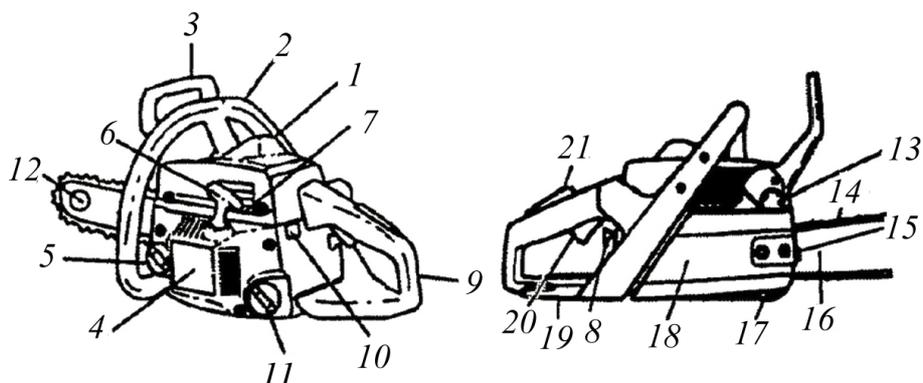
Бензопила «Husqvarna»: 1 – крышка цилиндра; 2 – передняя рукоятка; 3 – ручка тормоза; 4 – крышка стартера; 5 – резервуар цепного масла; 6 – ручка стартера; 7 – винт регулировки карбюратора; 8 – рычаг воздушной заслонки; 9 – задняя рукоятка; 10 – выключатель зажигания; 11 – топливный резервуар; 12 – концевая звездочка шины; 13 – глушитель; 14 – цепь пилы; 15 – винт натяжения цепи; 16 – направляющая шина; 17 – цепеуловитель; 18 – крышка сцепления; 19 – щиток для защиты правой руки; 20 – рычаг управления дросселем; 21 – рычаг блокировки дросселя
